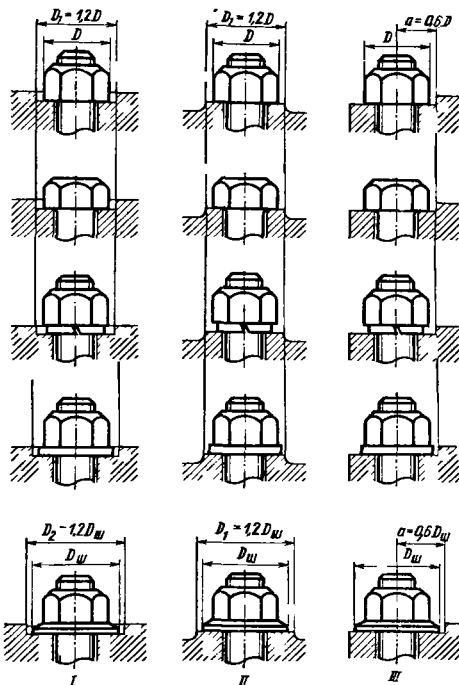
Размеры опорных поверхностей под гайку и головки болтов
